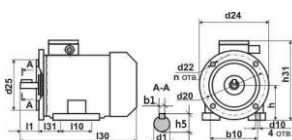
Габаритно-установочные и присоединительные размеры двигателя АИР56В4У3
